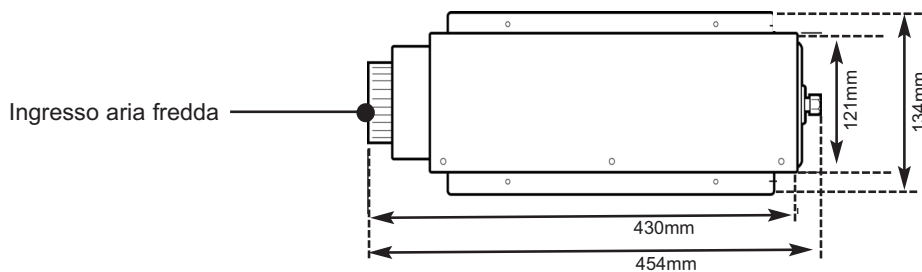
Installazione all'interno – Vista in pianta - SH2202 o SC2202
